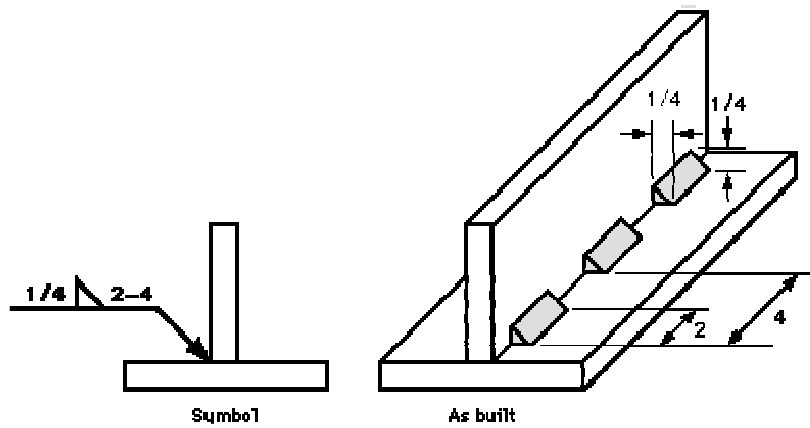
Aplicación de símbolos de soldadura de filete
